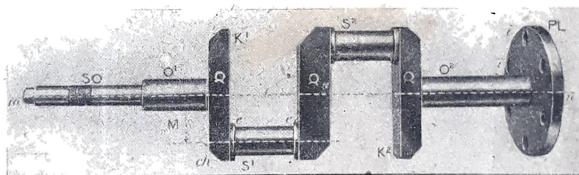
Collo d'oca per motore a due cilindri a  $180^\circ$
